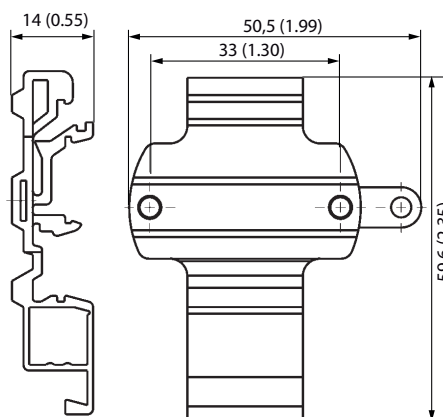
Dimensões do adaptador para calha DIN (7NG3092-8KA)
